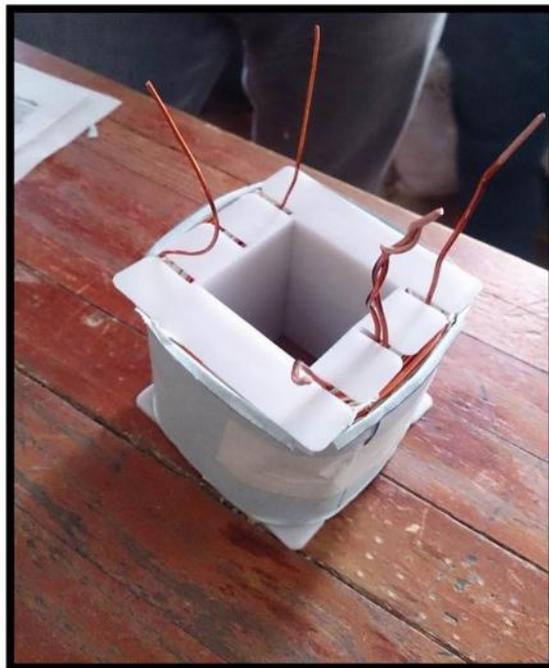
Primer devanado aislado con papel parafinado.
